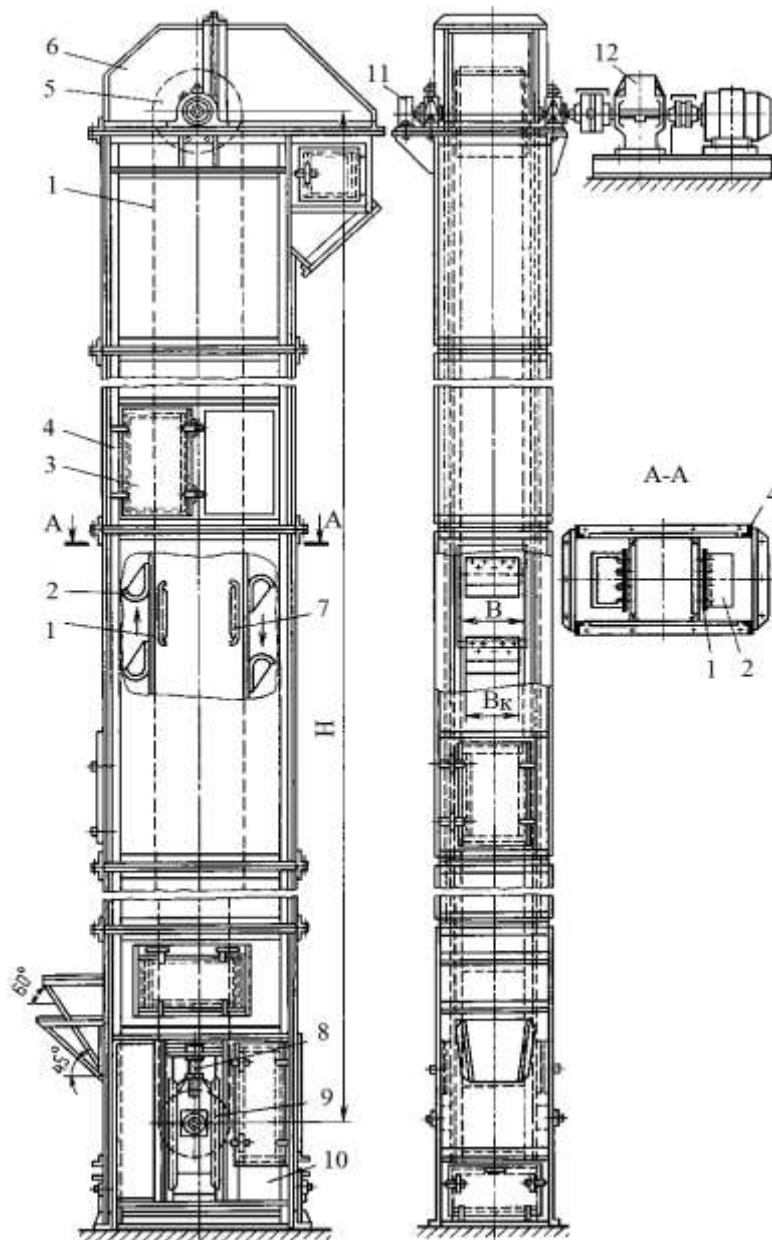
Вертикальний ківшевий стрічковий елеватор
